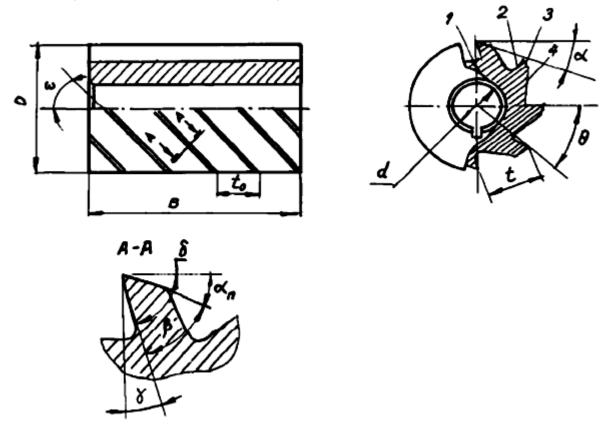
Конструкция и геометрия цилиндрической фрезы
